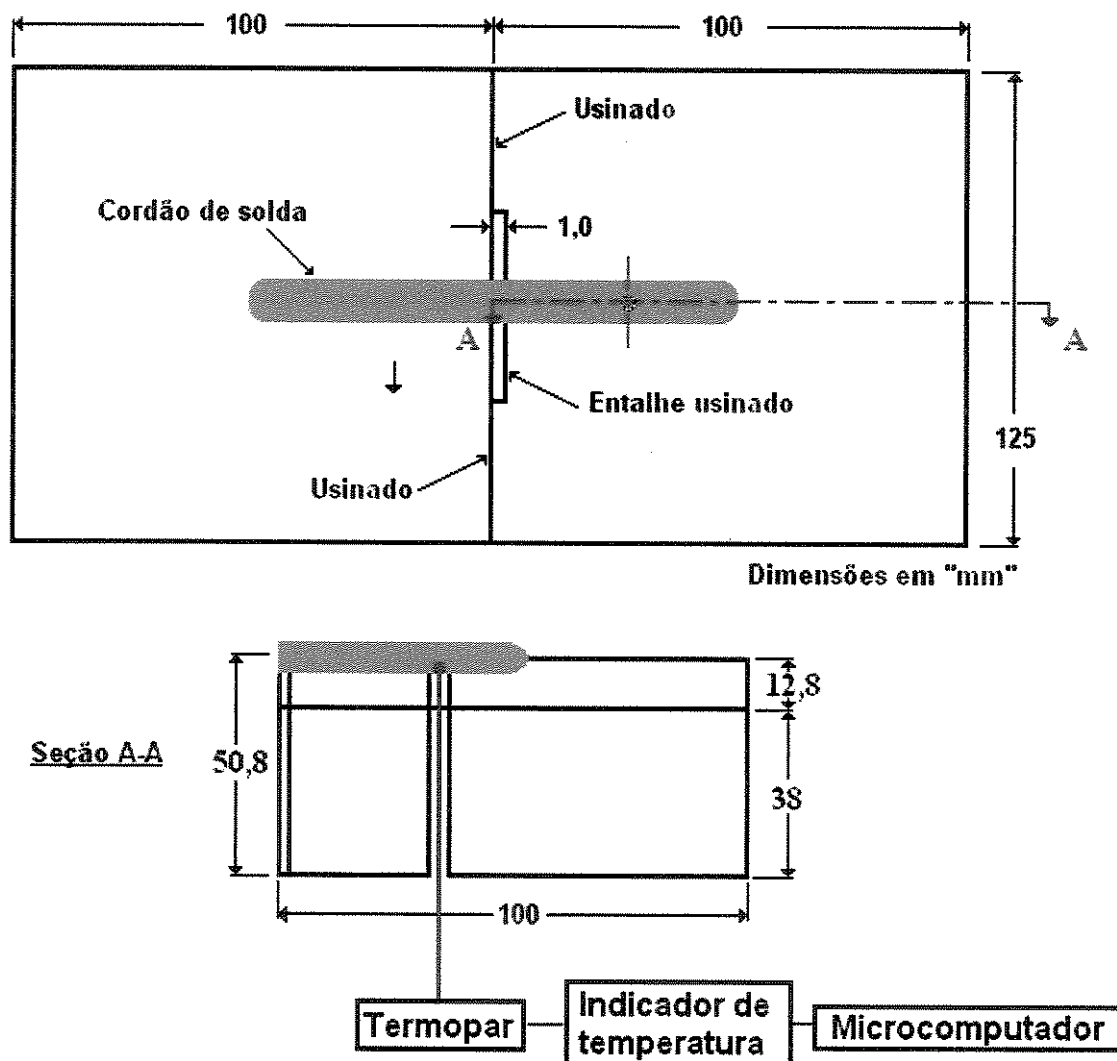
Local de posicionamento do termopar no metal de solda
